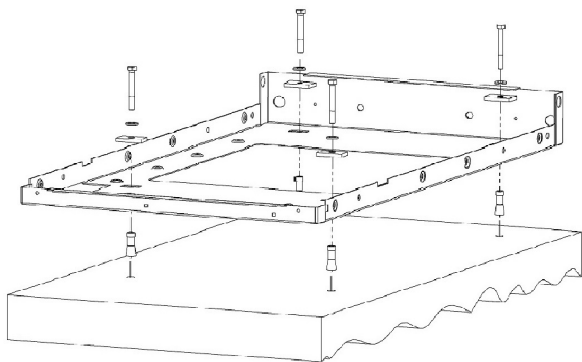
Fästa i golvet – Metod A – installation på C-profil för betonggolv.
